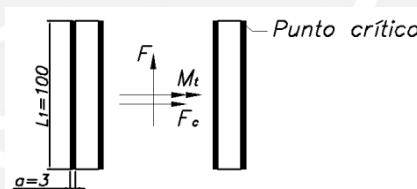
Cargas actuantes en los cordones de soldadura del soporte del reactor
